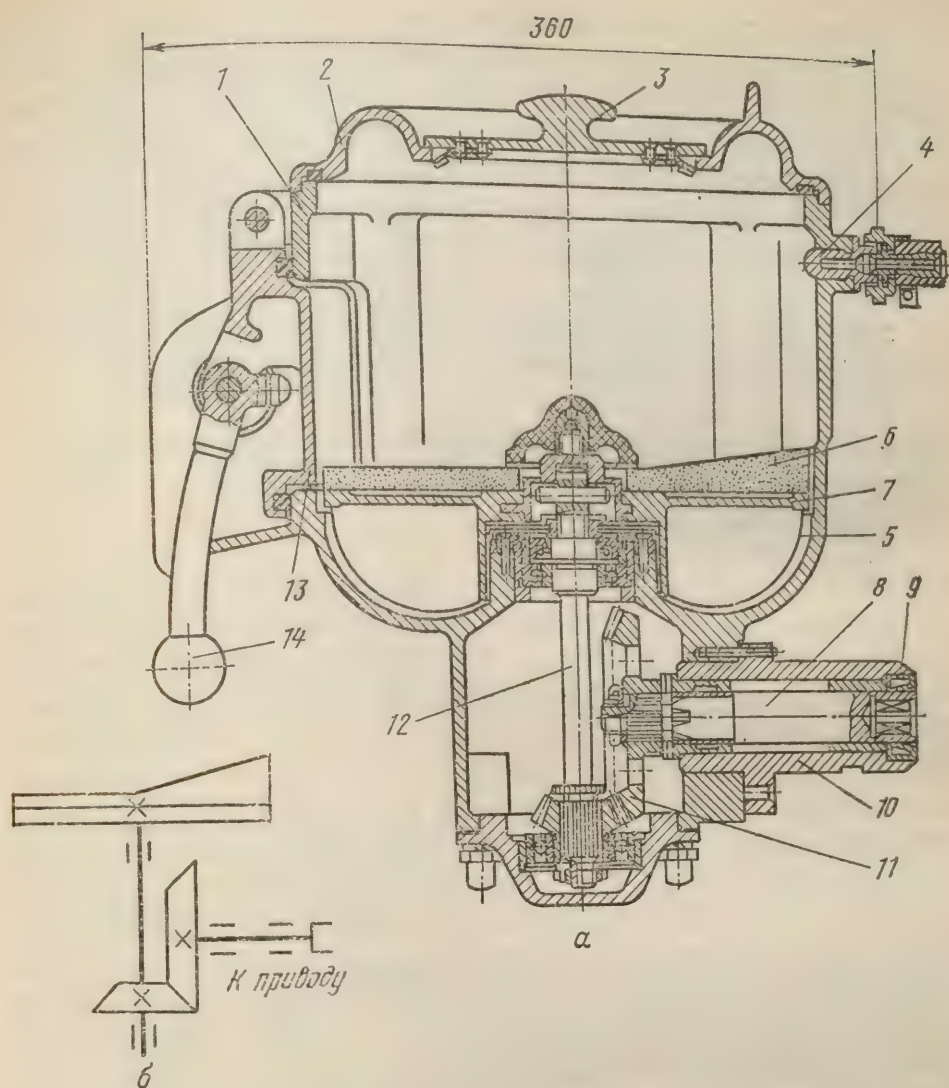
Сменный картофелеочистительный механизм УММ-5:
